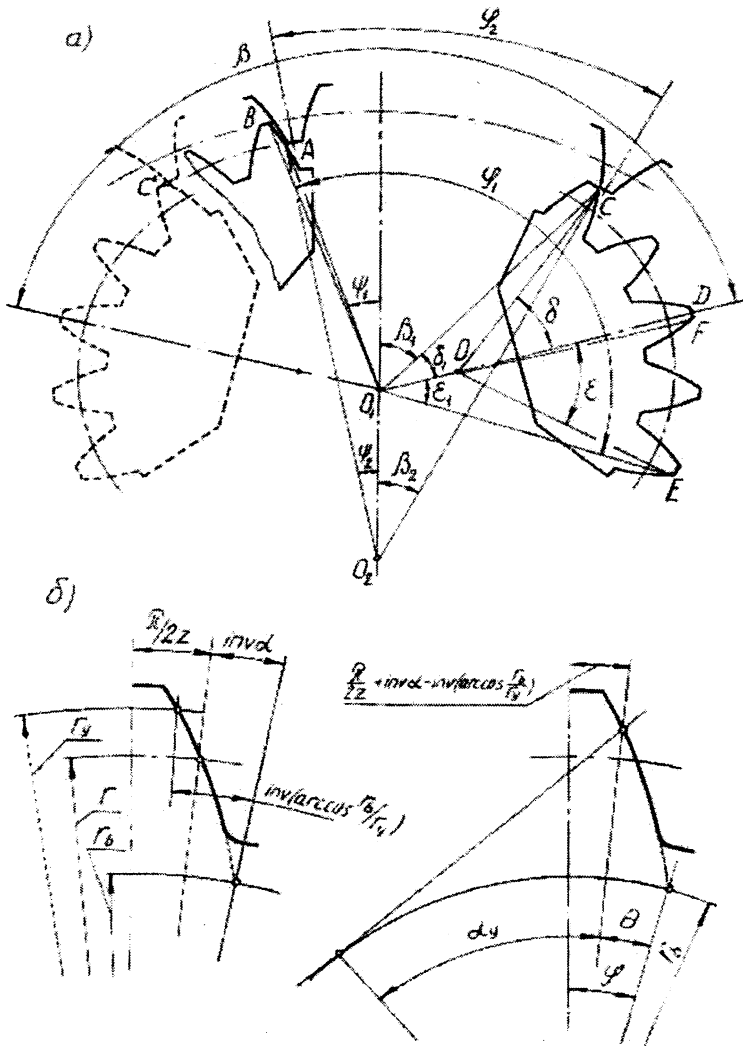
Схема взаимодействия составного и цельного зубчатых колес
